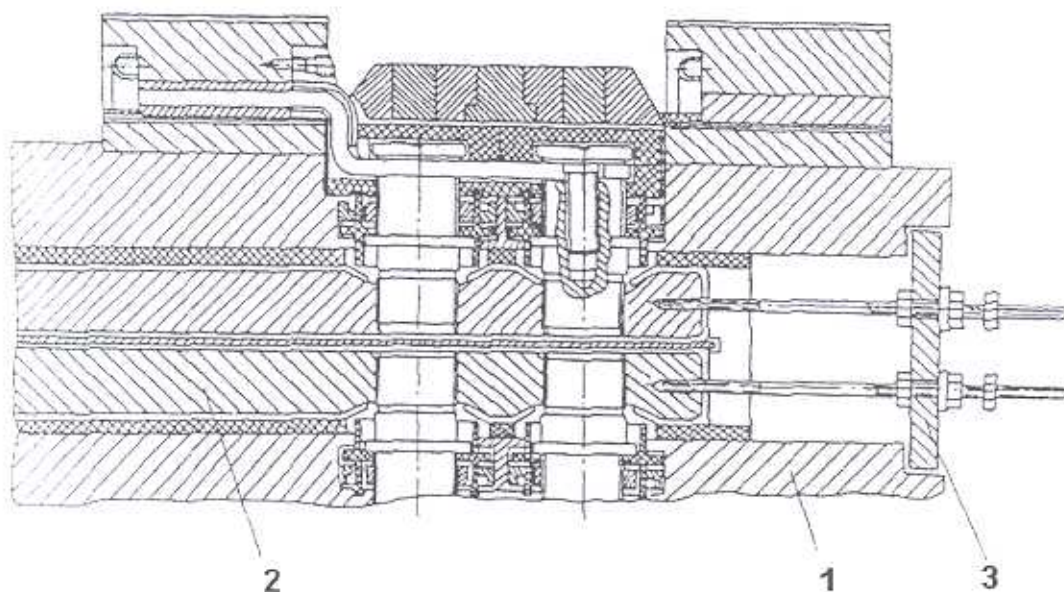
Приспособление для выемки внутреннего токоподвода: 1 – вал ротора, 2 – стержень токоподвода, 3 – приспособление.
